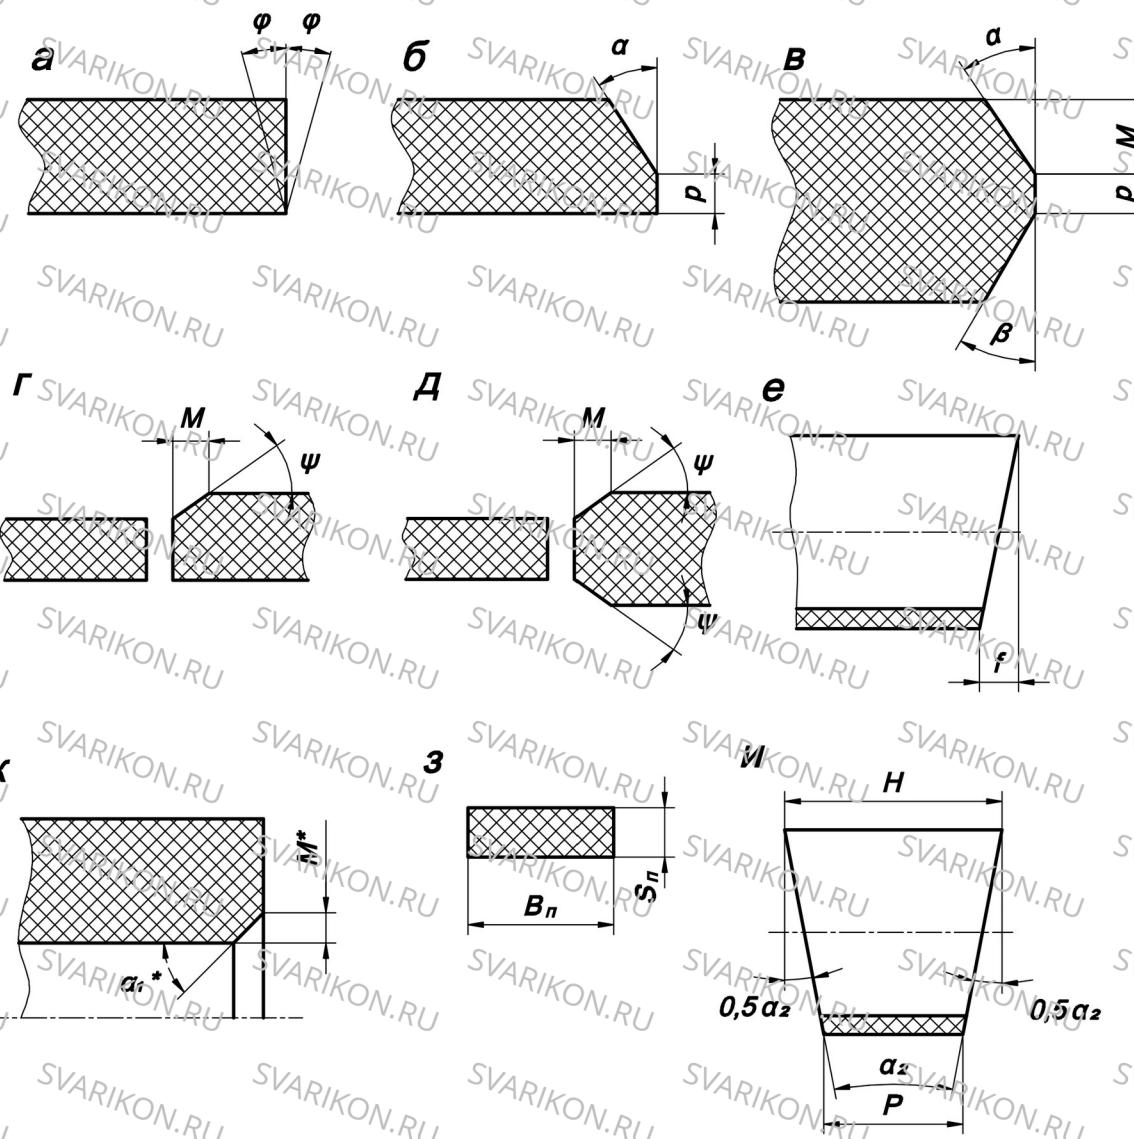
Размеры, контролируемые измерением при подготовке деталей под сварку:
